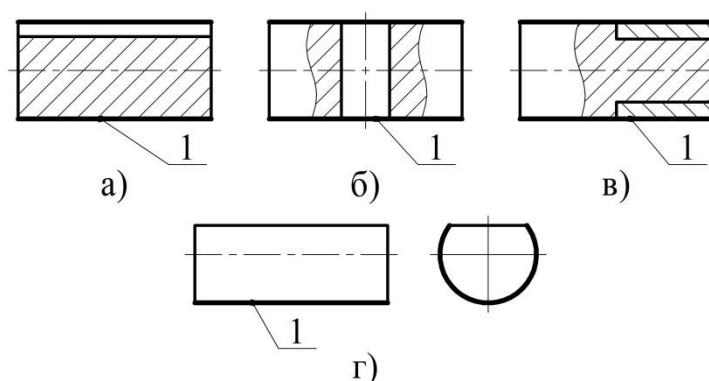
Группа деталей с общей операцией точения базовой поверхности:
